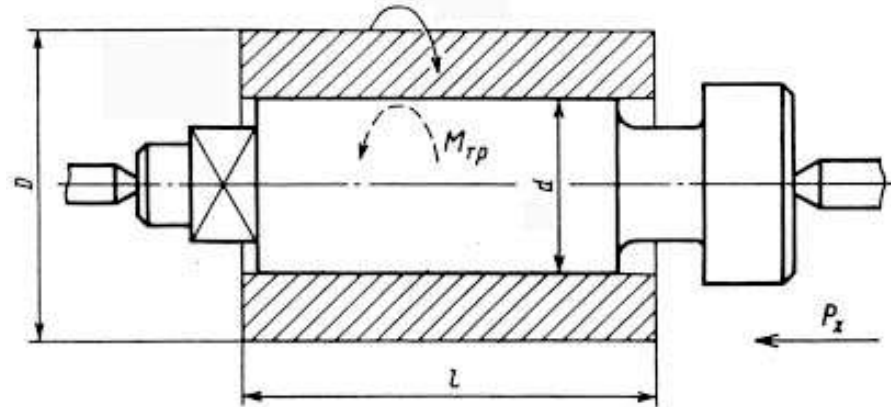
Оправка для заготовок, які встановлюються під пресом:
